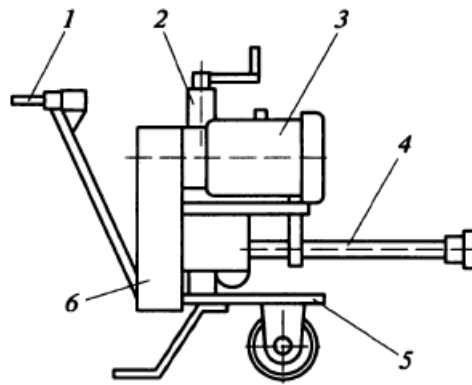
Схема гайковерта для крепления колес: 1 — пульт управления; 2 — механизм подъема и опускания; 3 — электродвигатель; 4 — выходной вал; 5 — основание; 6 — приводной механизм
